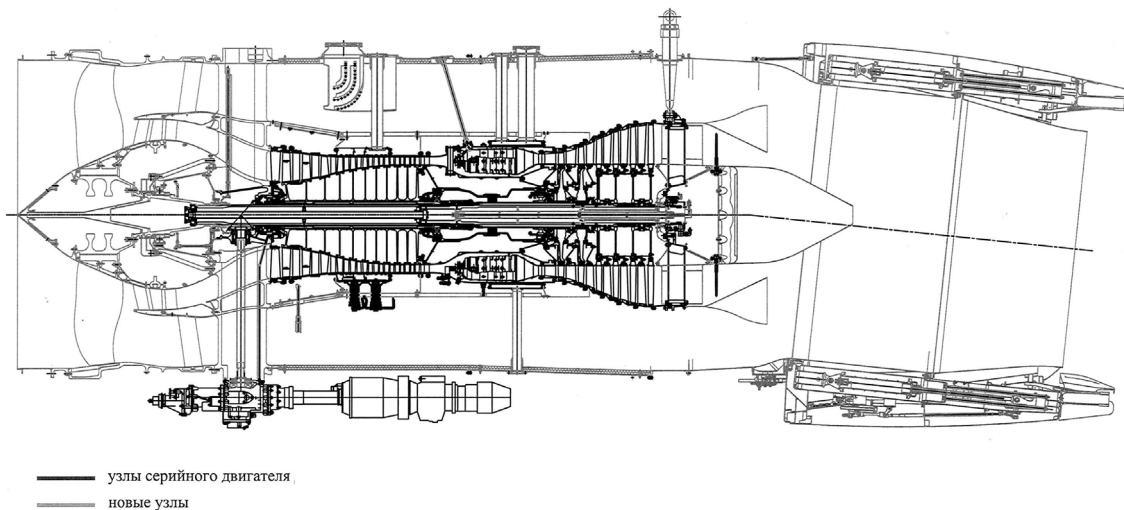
Общий вид двигателя Д-30КП «Бурлак»
